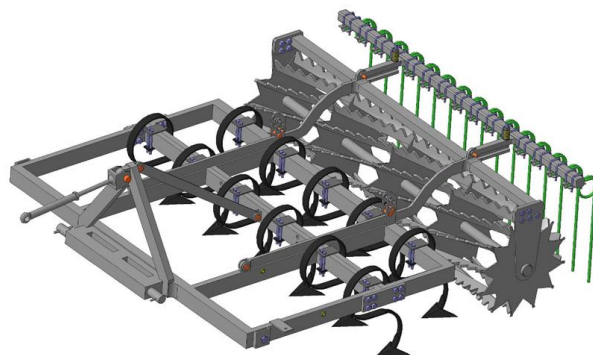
3D модель почвообрабатывающего агрегата
